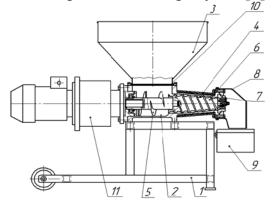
Шнековый экструдергранулятор: 1 — рама; 2 — приемная камера; 3 — приемный бункер; 4 — рабочая камера; 5 — подающий шнек; 6 — прессующий шнек; 7 — узелпрессования; 8 — короб; 9 — сборник; 10 — заслонка; 11 — моторредуктор
